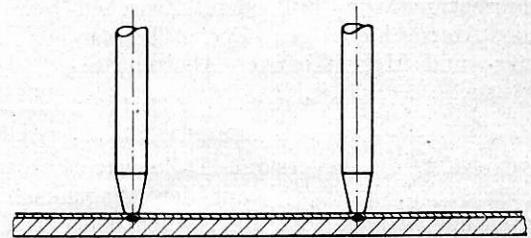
Punktschweißung mit parallel stehenden Schweißelektroden.
